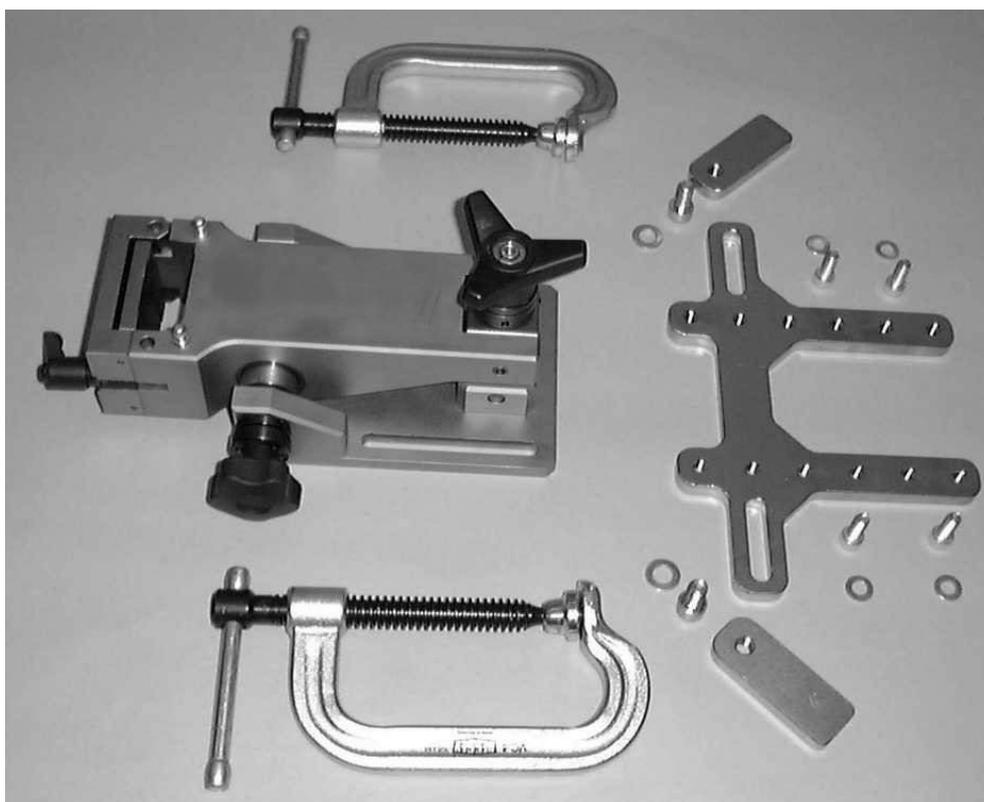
Адаптер регулировки наклона с опорной пластиной и стандартными зажимными элементами
